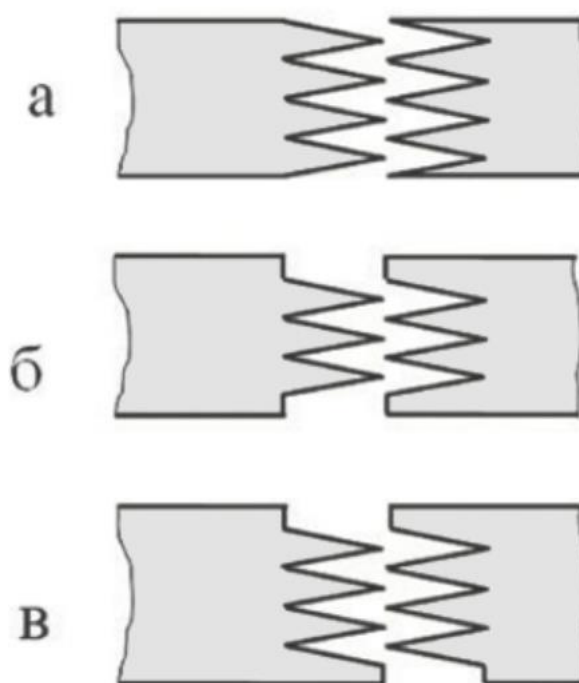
Виды профиля зубчато-клинового соединения
